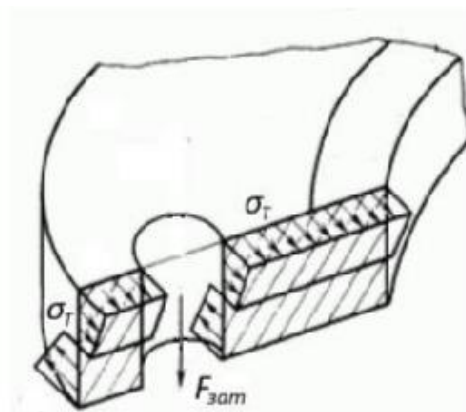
Уточняющая расчётная схема фланцевого соединения крышки с корпусом
